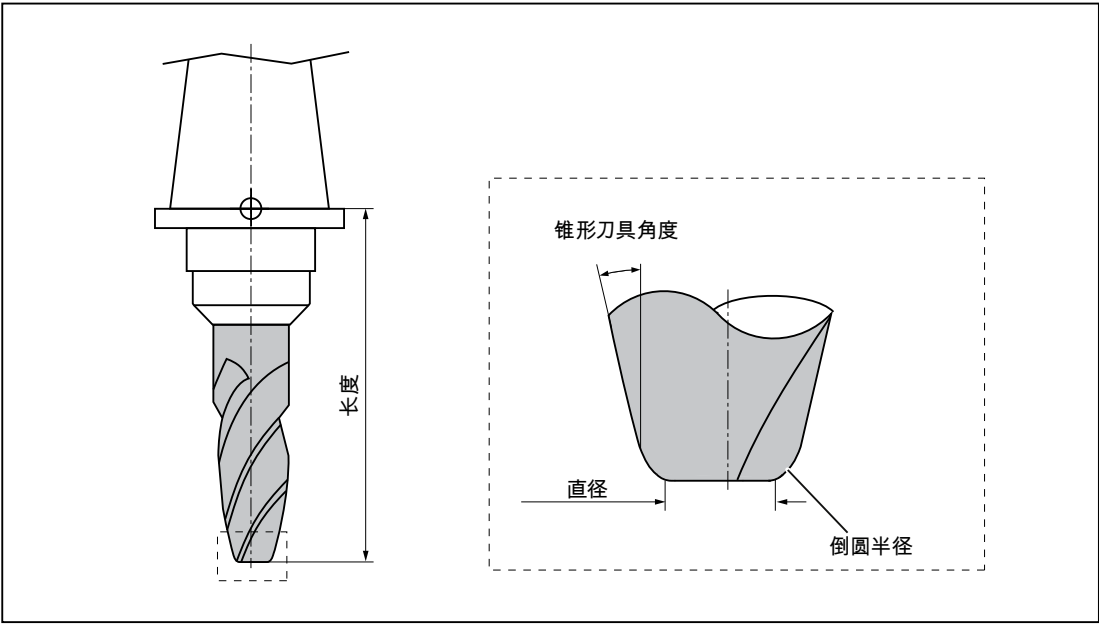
3D 刀具，例如：带倒圆的截锥铣刀（156 型）
